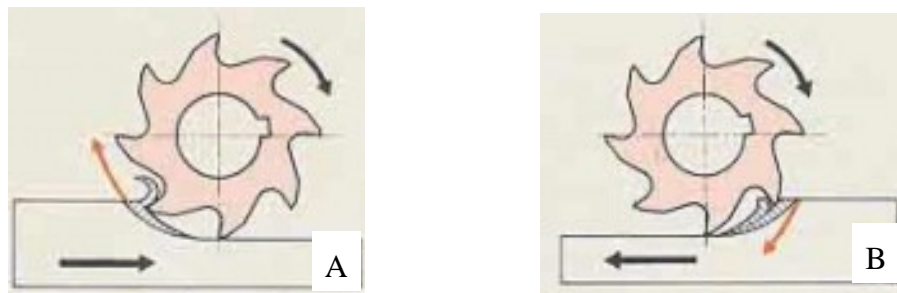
Fresagem cilíndrica discordante (A) e concordante (B) <sup>12</sup>
